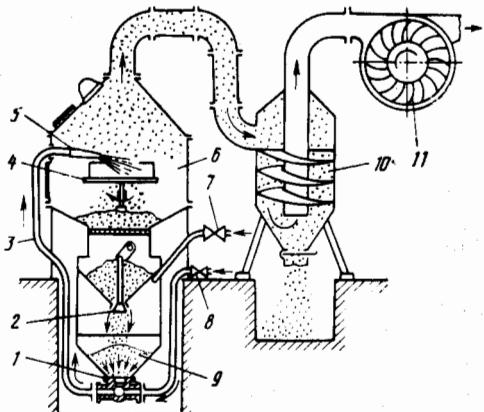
Схема установки для очистки деталей косточковой крошкой:
